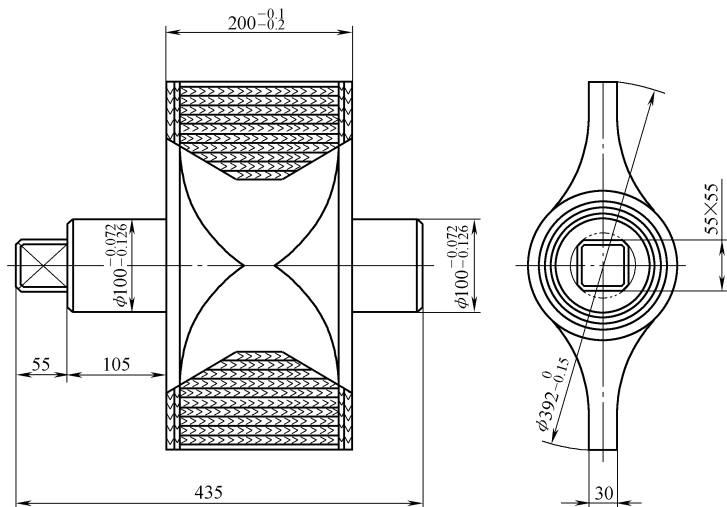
板阀堆焊后的加工部位及尺寸
